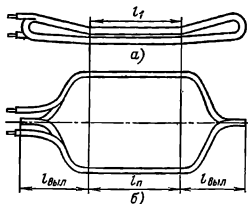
Катушка двухслойной обмотки статора. Общий вид.
